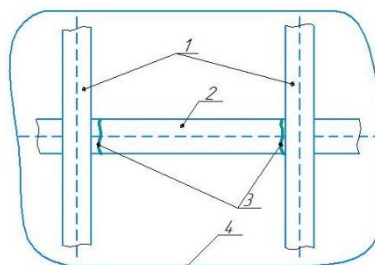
Разрушение сварных швов, соединяющих полки стрингеров и шпангоутов. 1 - шпангоуты; 2 - стрингер; 3 - трещина; 4 - обшивка.
